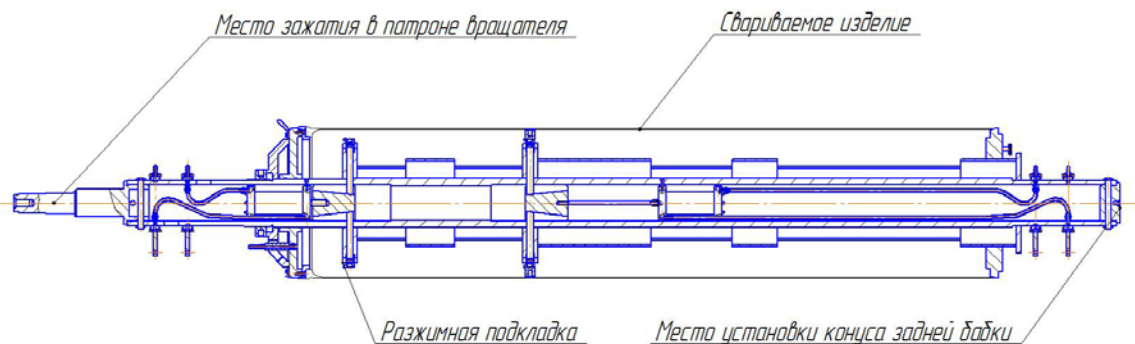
Оправка для сборки, сварки, и центровки обечаек и приварки к ним шпангоутов
